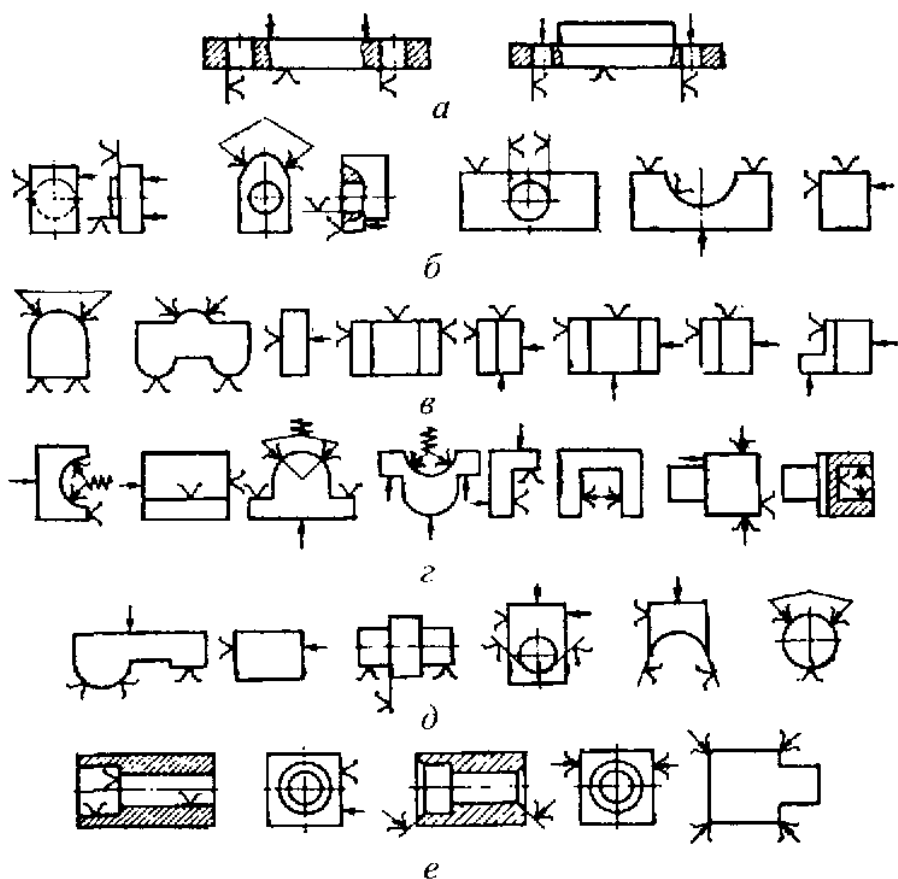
Схеми встановлення оброблених заготовок в пристроях АВ і АЛ
